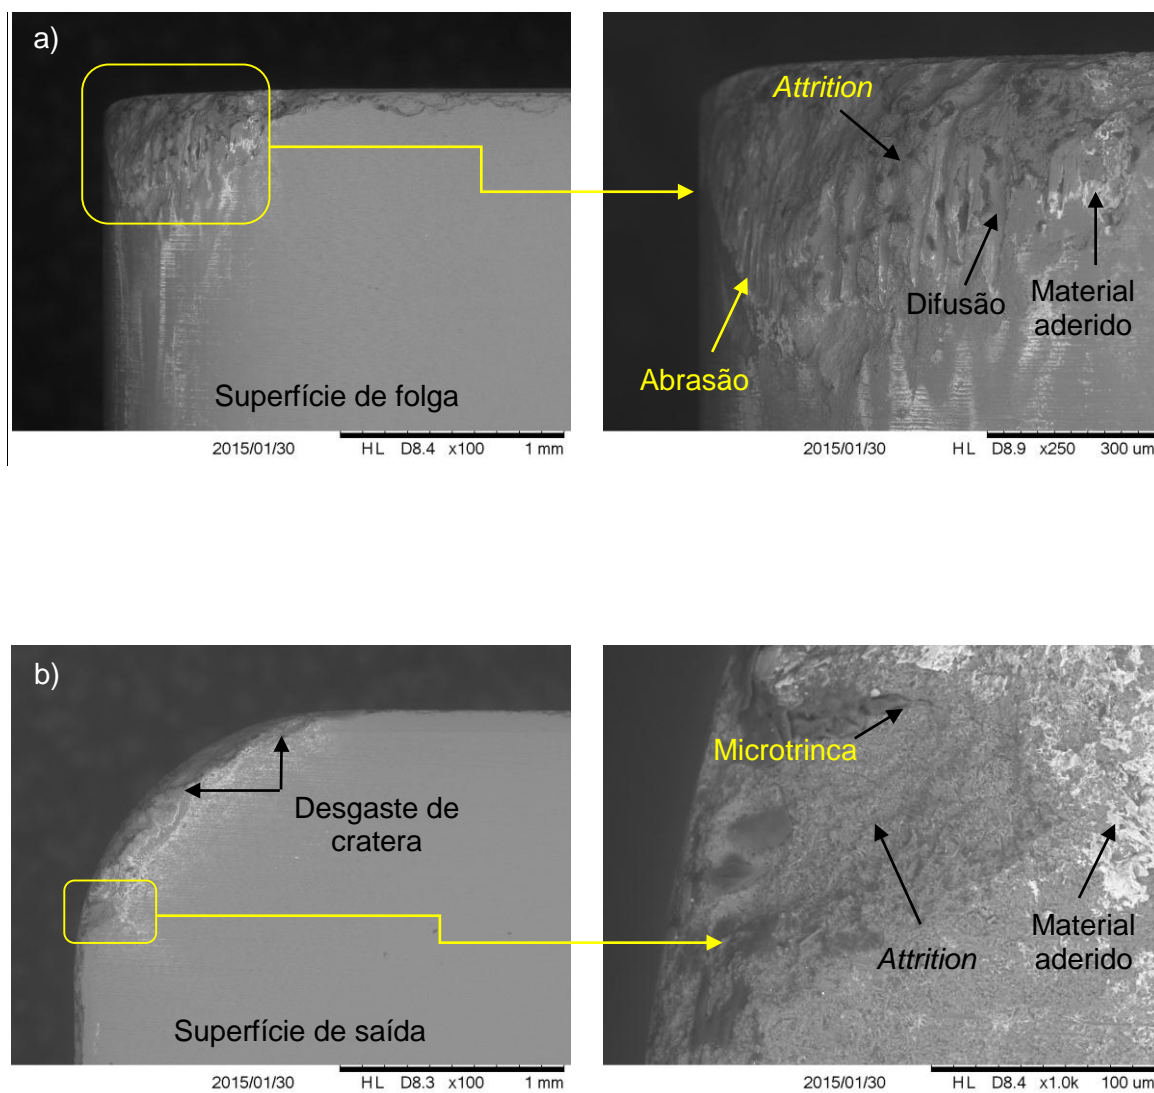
Fotografias obtidas através do MEV das ferramentas SiAlON após a usinagem do Inconel 718 com aplicação de fluido de corte LB 2000 por MQF. (a) superfície de folga e (b) superfície de saída
